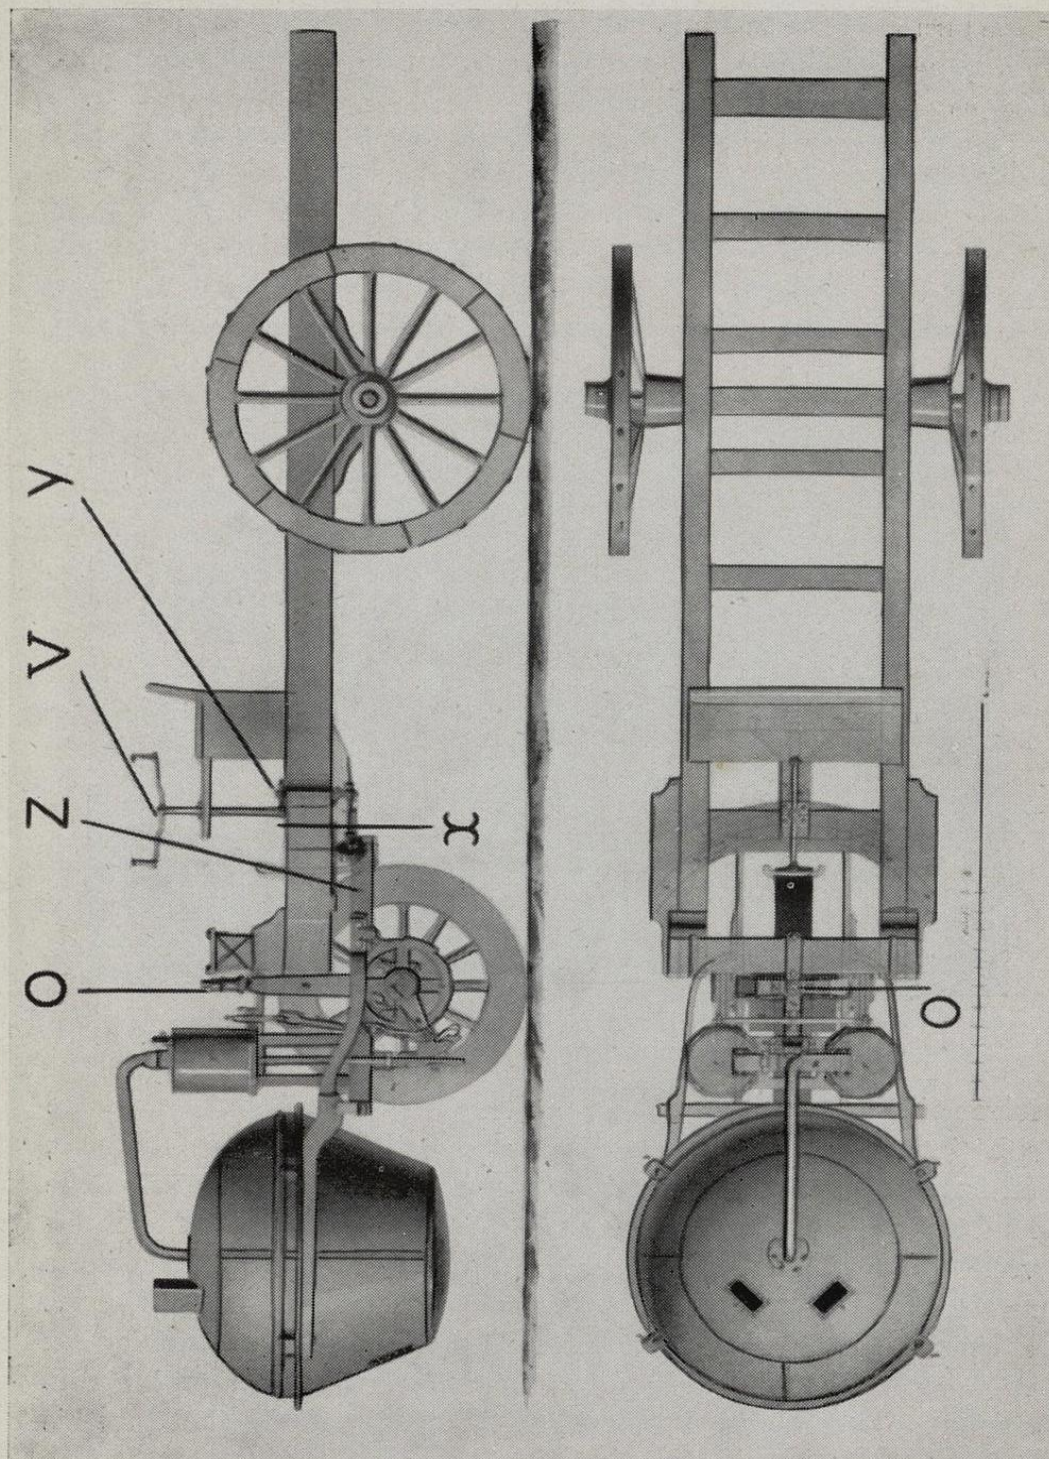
Reproduction des planches originales ; plan et élévation du véhicule.
